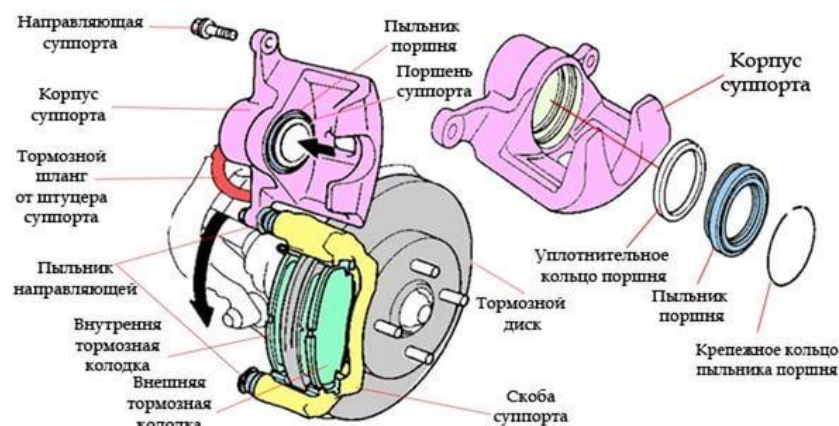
Однопоршневой тормозной механизм с плавающей скобой
